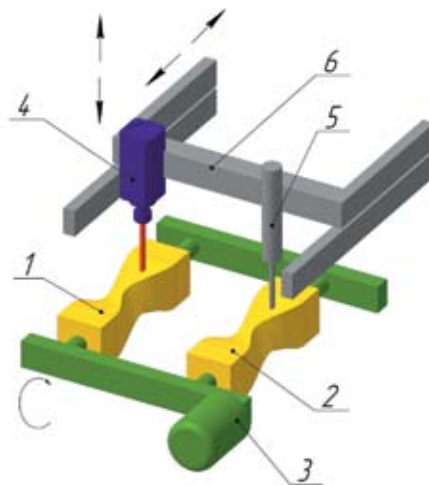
Фрезерный станок для объемного фрезерования по копиру:
